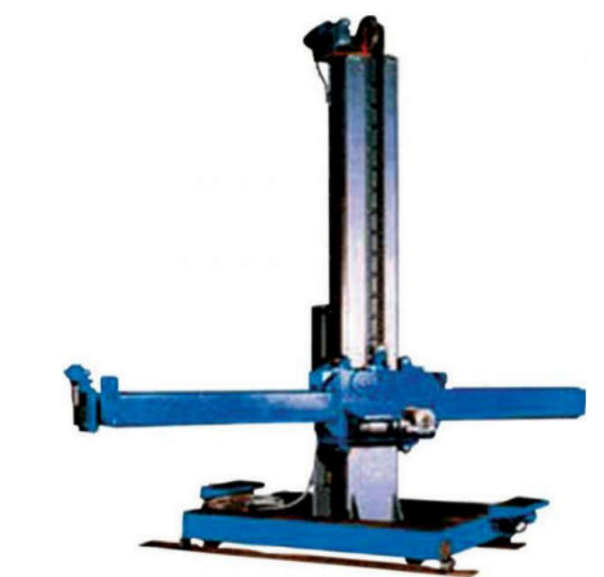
Загальний вид зварювальної колони BCZQ 2x2
